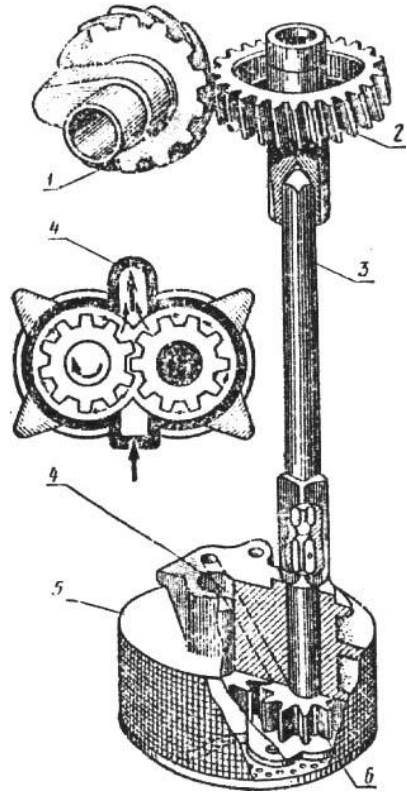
Шестерний оливний насос двигунів К-750 і «Урал»:
